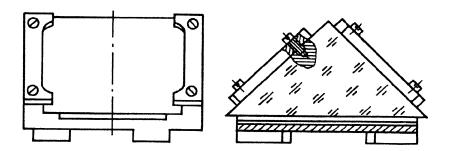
Крепление призмы БР-180 прижимными планками
